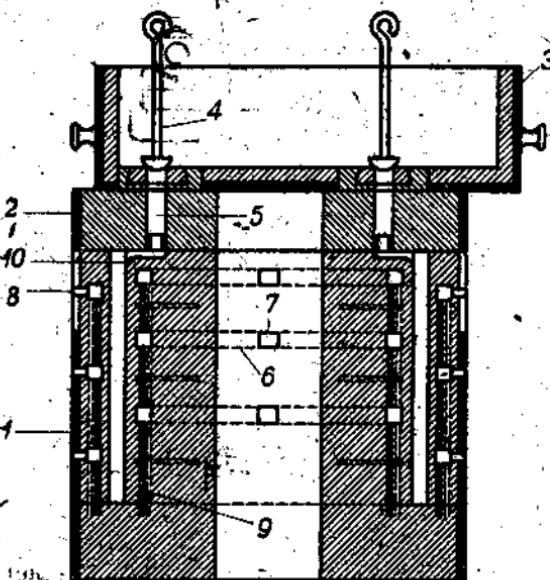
Отливка заготовки для поршневых колец в опоках.
